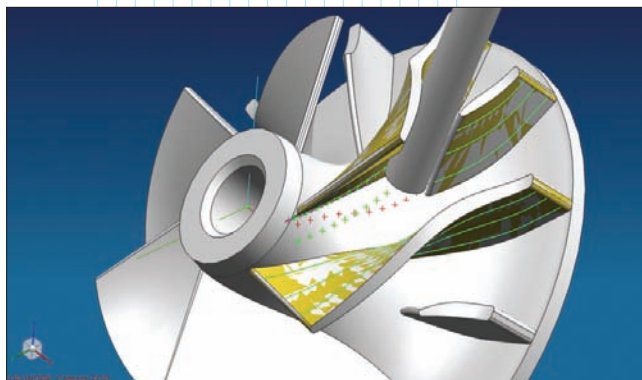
Фрезерование торцевым инструментом при изготовлении моноколеса
